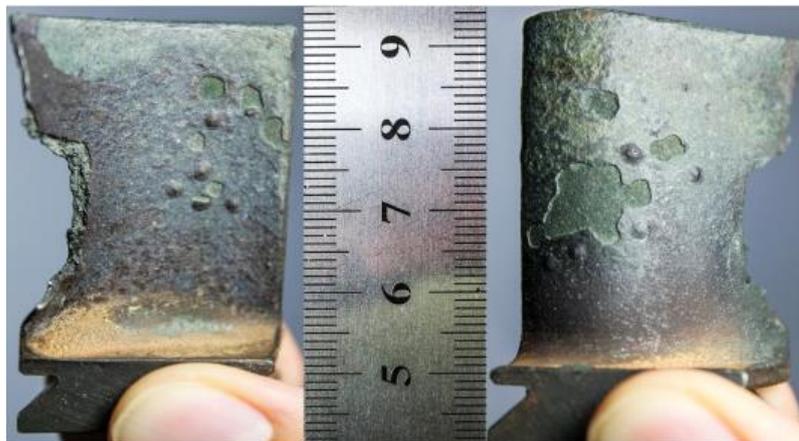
Коррозионное разрушение сопел первой ступени газовой компрессора
